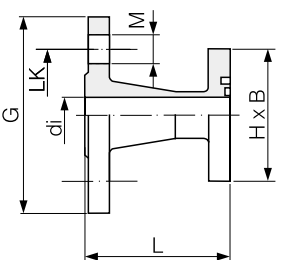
Dimensiones de la parte frontal del sensor DN 2...25
